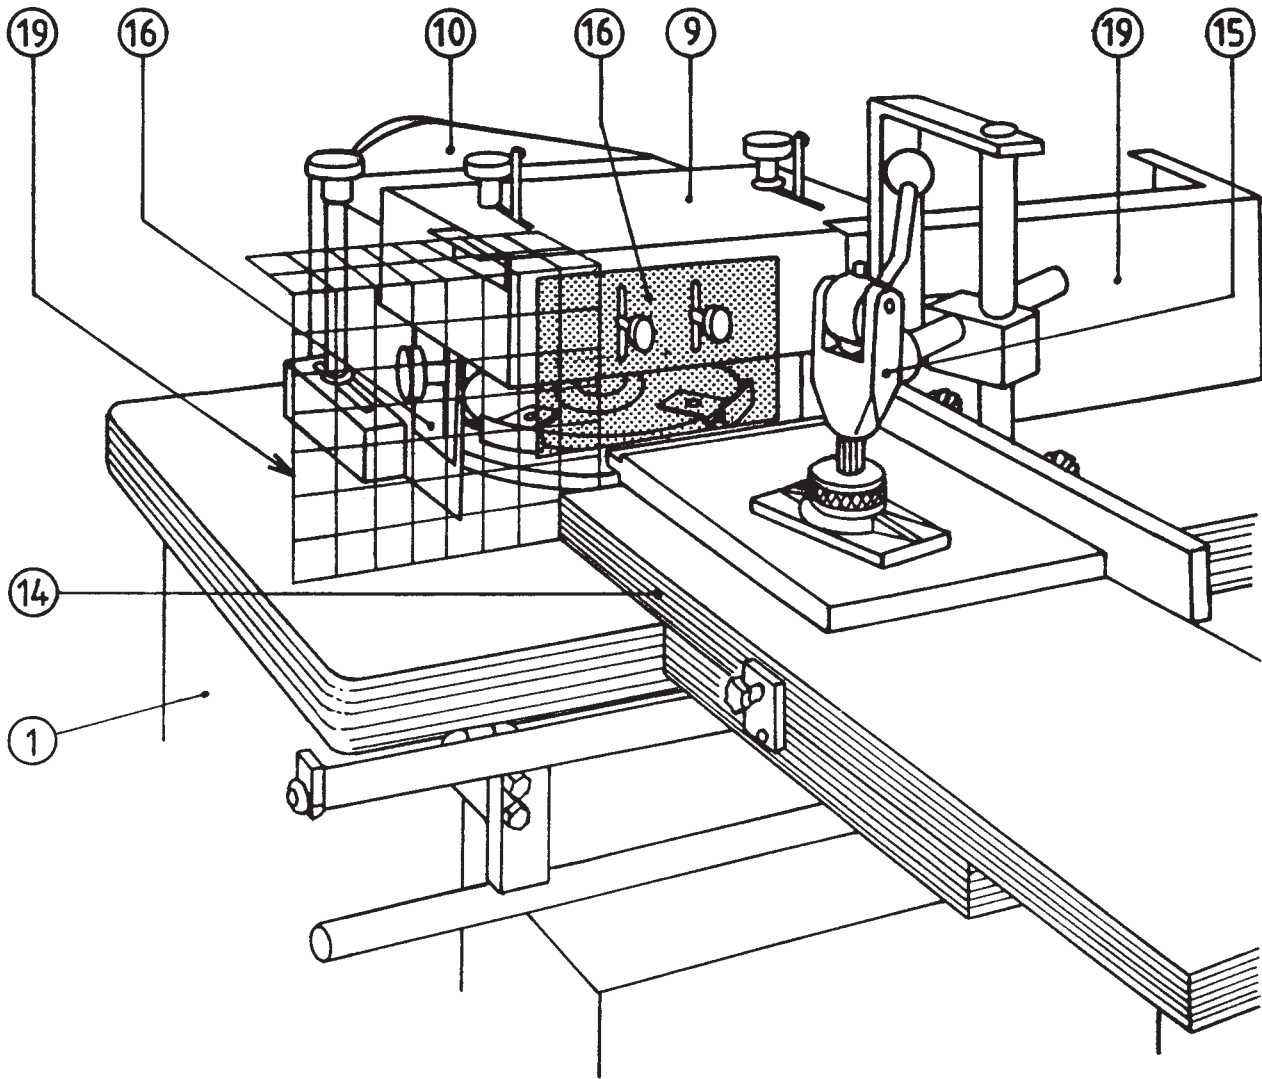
Einspindelige senkrechte Tischfräsmaschine ausgerüstet zum Zapfenschneiden/Schlitten
